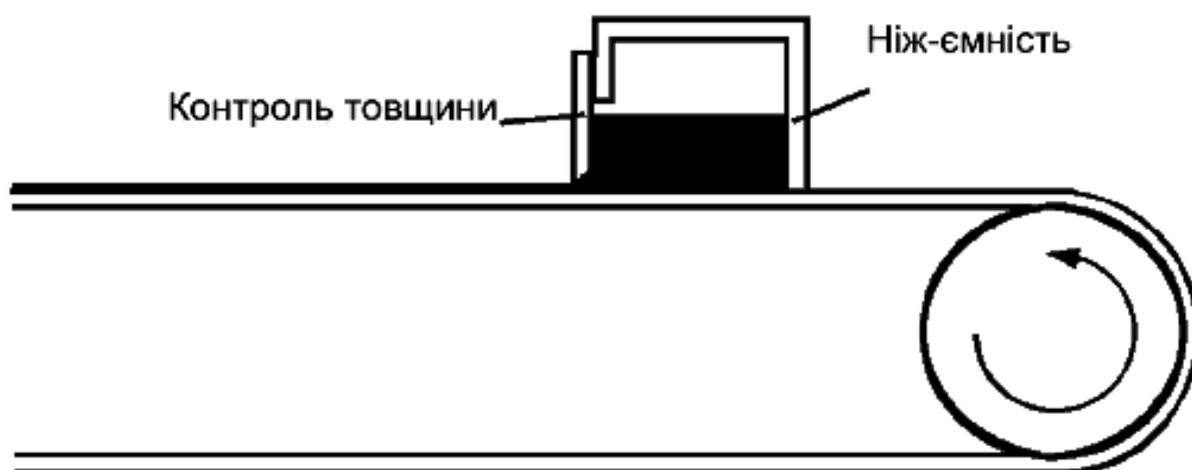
Схема нанесення товстої плівки методом *tape casting* [66]
